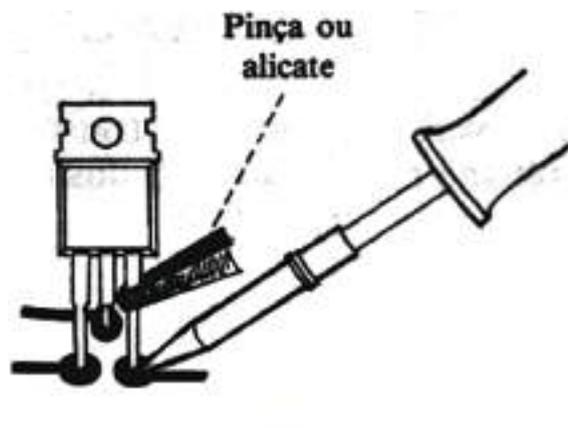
Exemplo de soldadura de um Circuito Integrado.
